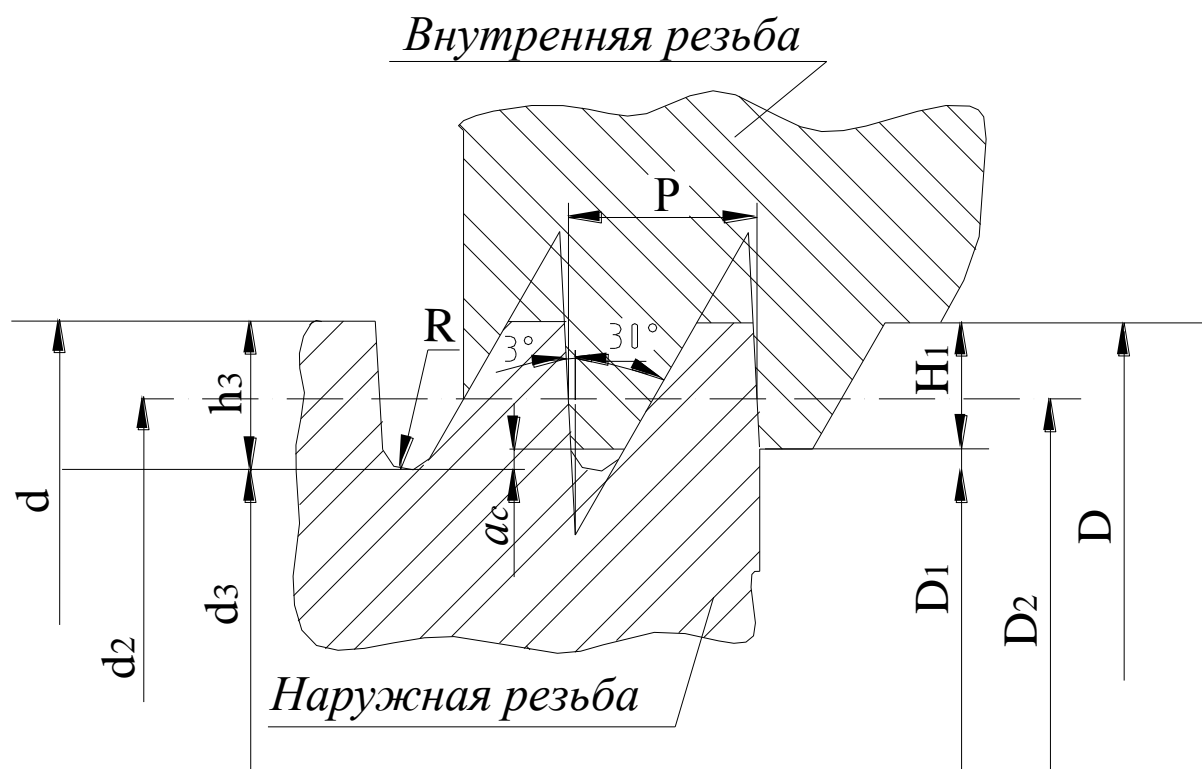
Номинальные профили наружной и внутренней упорной резьбы
